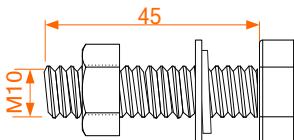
Dimensões dos conjuntos para fixar em estrutura metálica (dimensões em mm)
